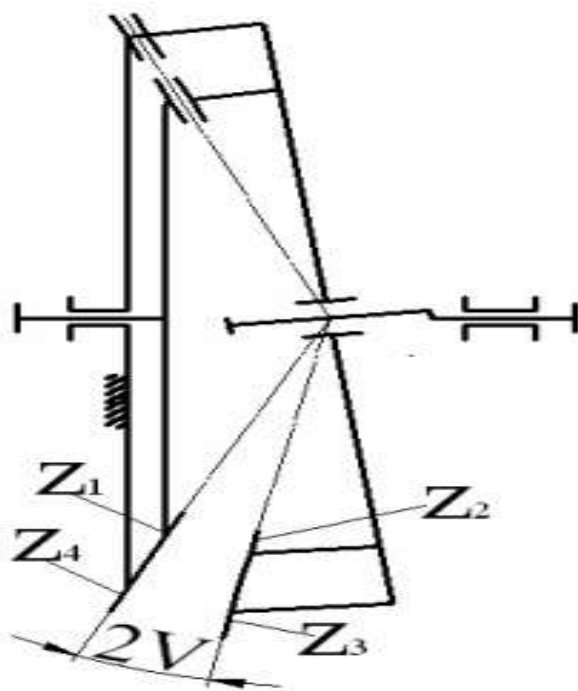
Кинематическая схема одноступенчатого редуктора
